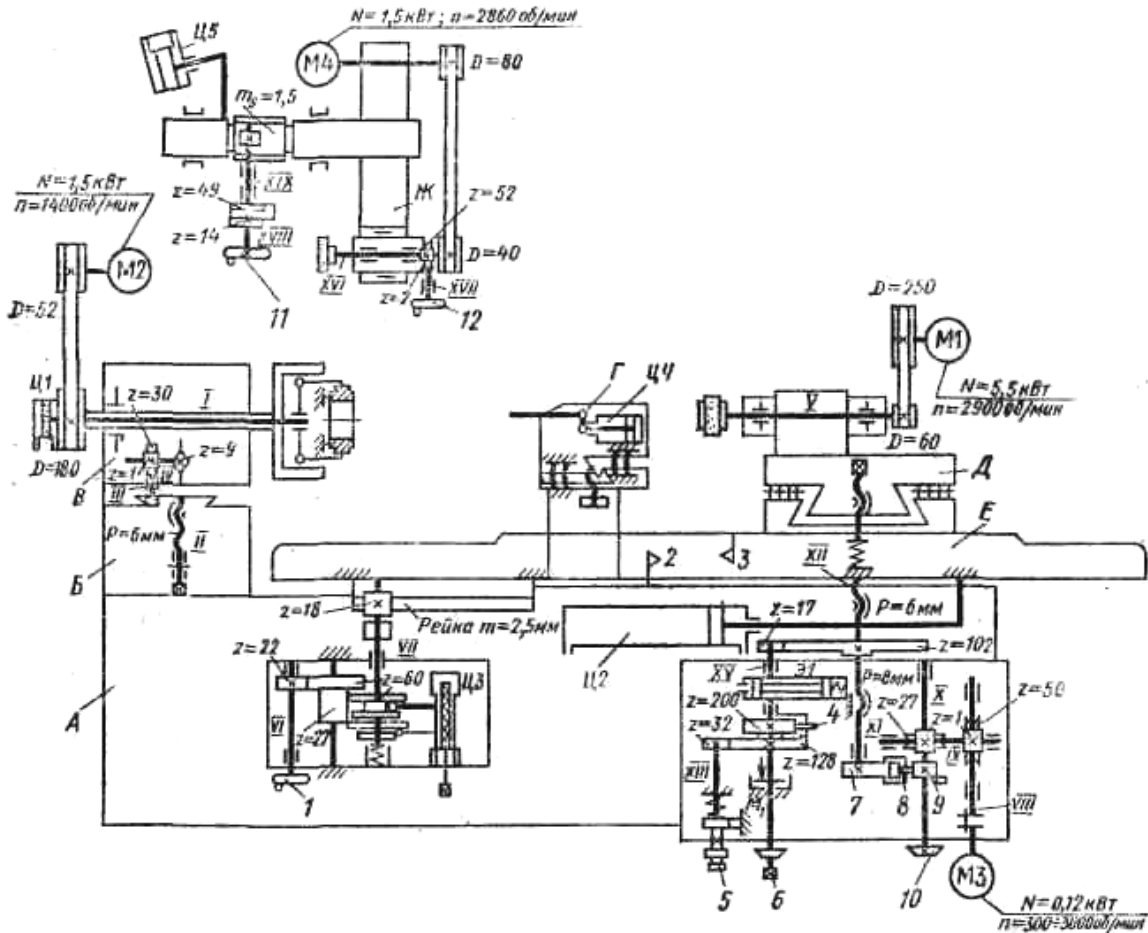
Кинематическая схема внутришлифовального станка модели 3К227Б
